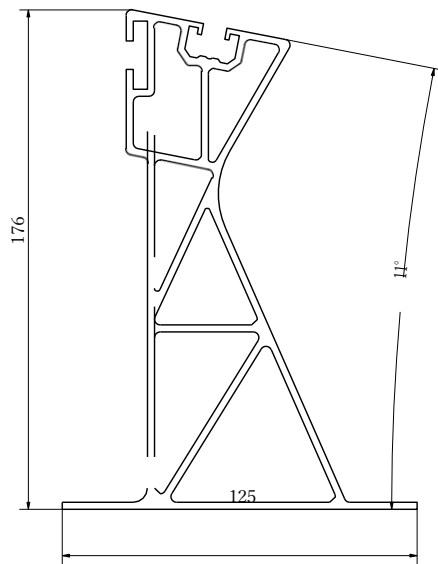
K-45-7 Aluminium-Montagehalterung, hoch
